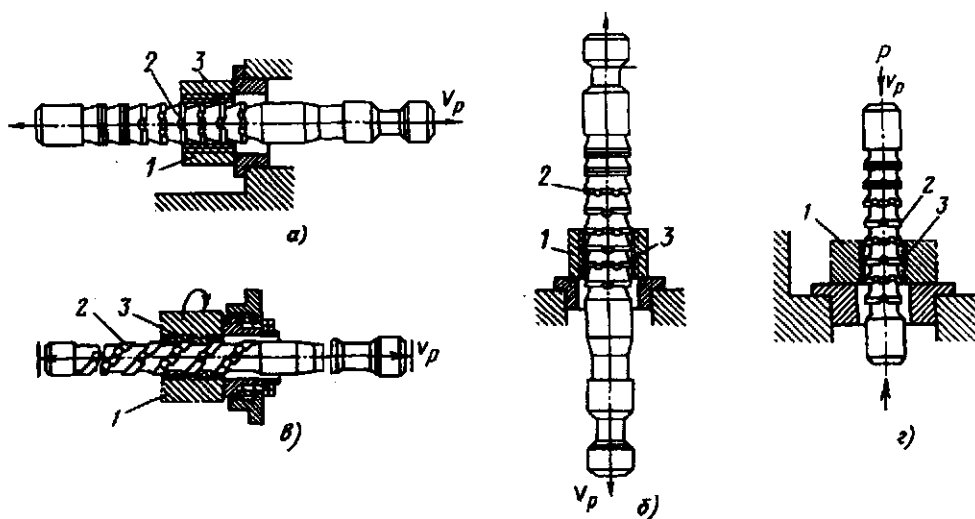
Виды внутреннего протягивания: 1 — деталь; 2 — протяжка; 3 — слои срезаемого металла; v_p — рабочий ход
